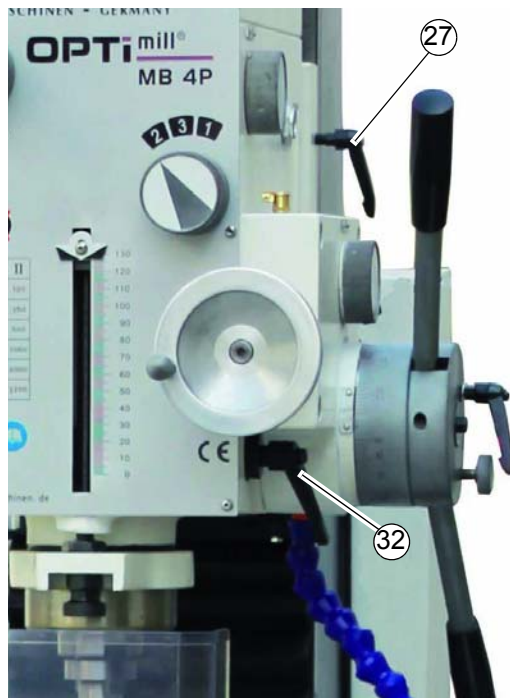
Bohr- Fräskopf für Pinolenvorschub mit dem Feinvorschub
